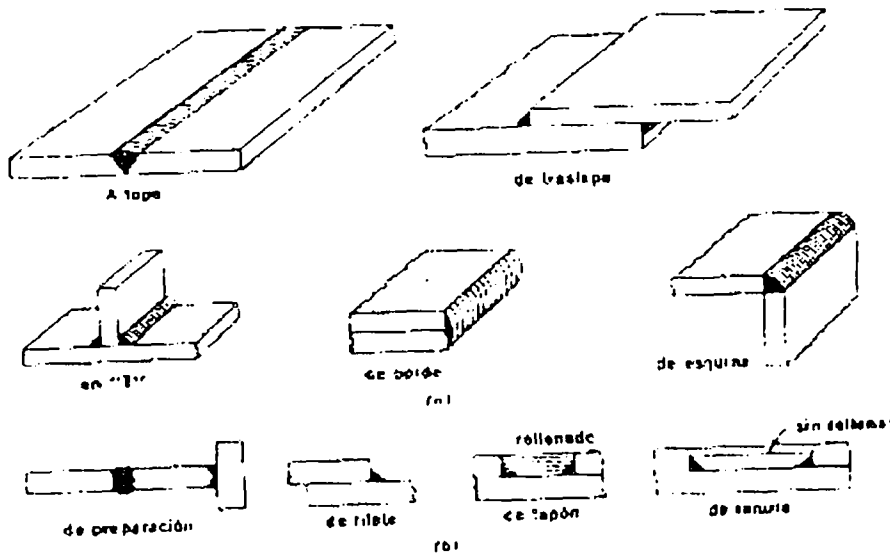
Conexiones soldadas (a) Tipo de juntas (b) Tipo de soldadura.
